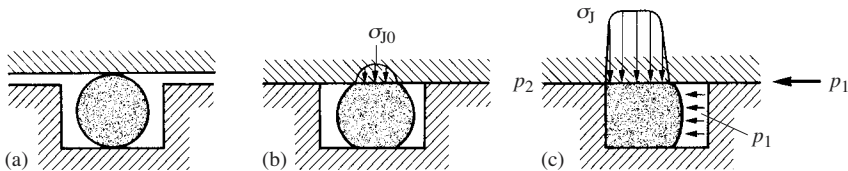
Joint torique : (a) avant serrage; (b) serrage initial; (c) mise sous pression.
